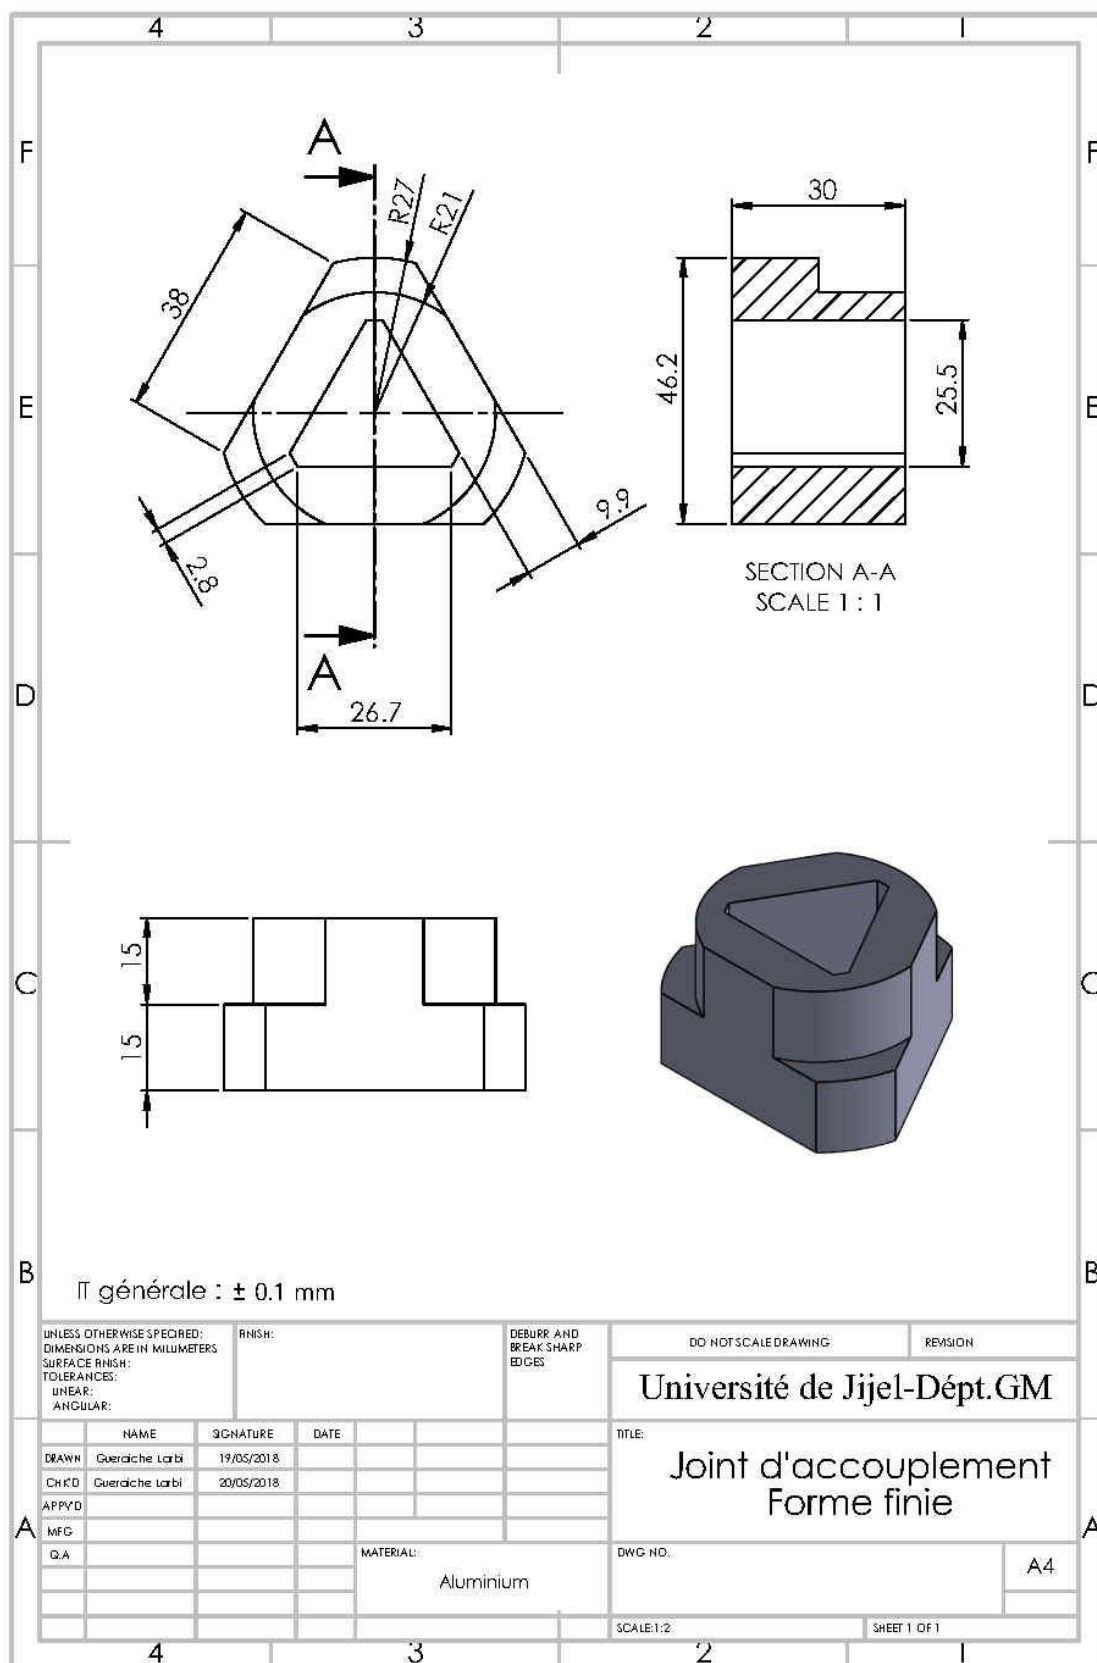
Dessin de définition du joint d'accouplement sous SolidWorks.
